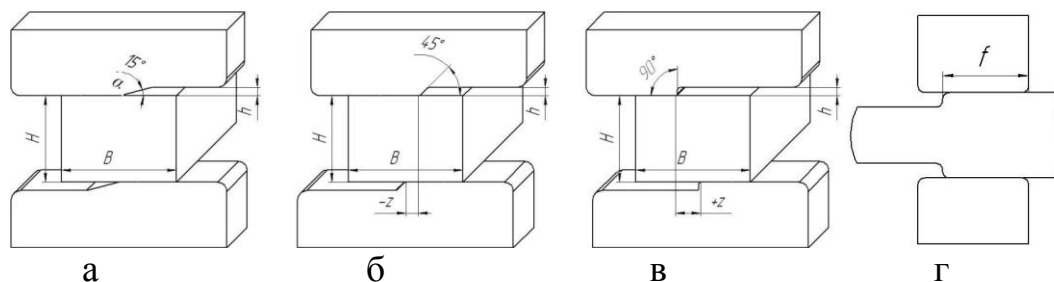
Схема обжима плоской заготовки ступенчатыми бойками: а – нулевой зазор, б – отрицательный зазор, в – положительный зазор, г – вид сбоку
